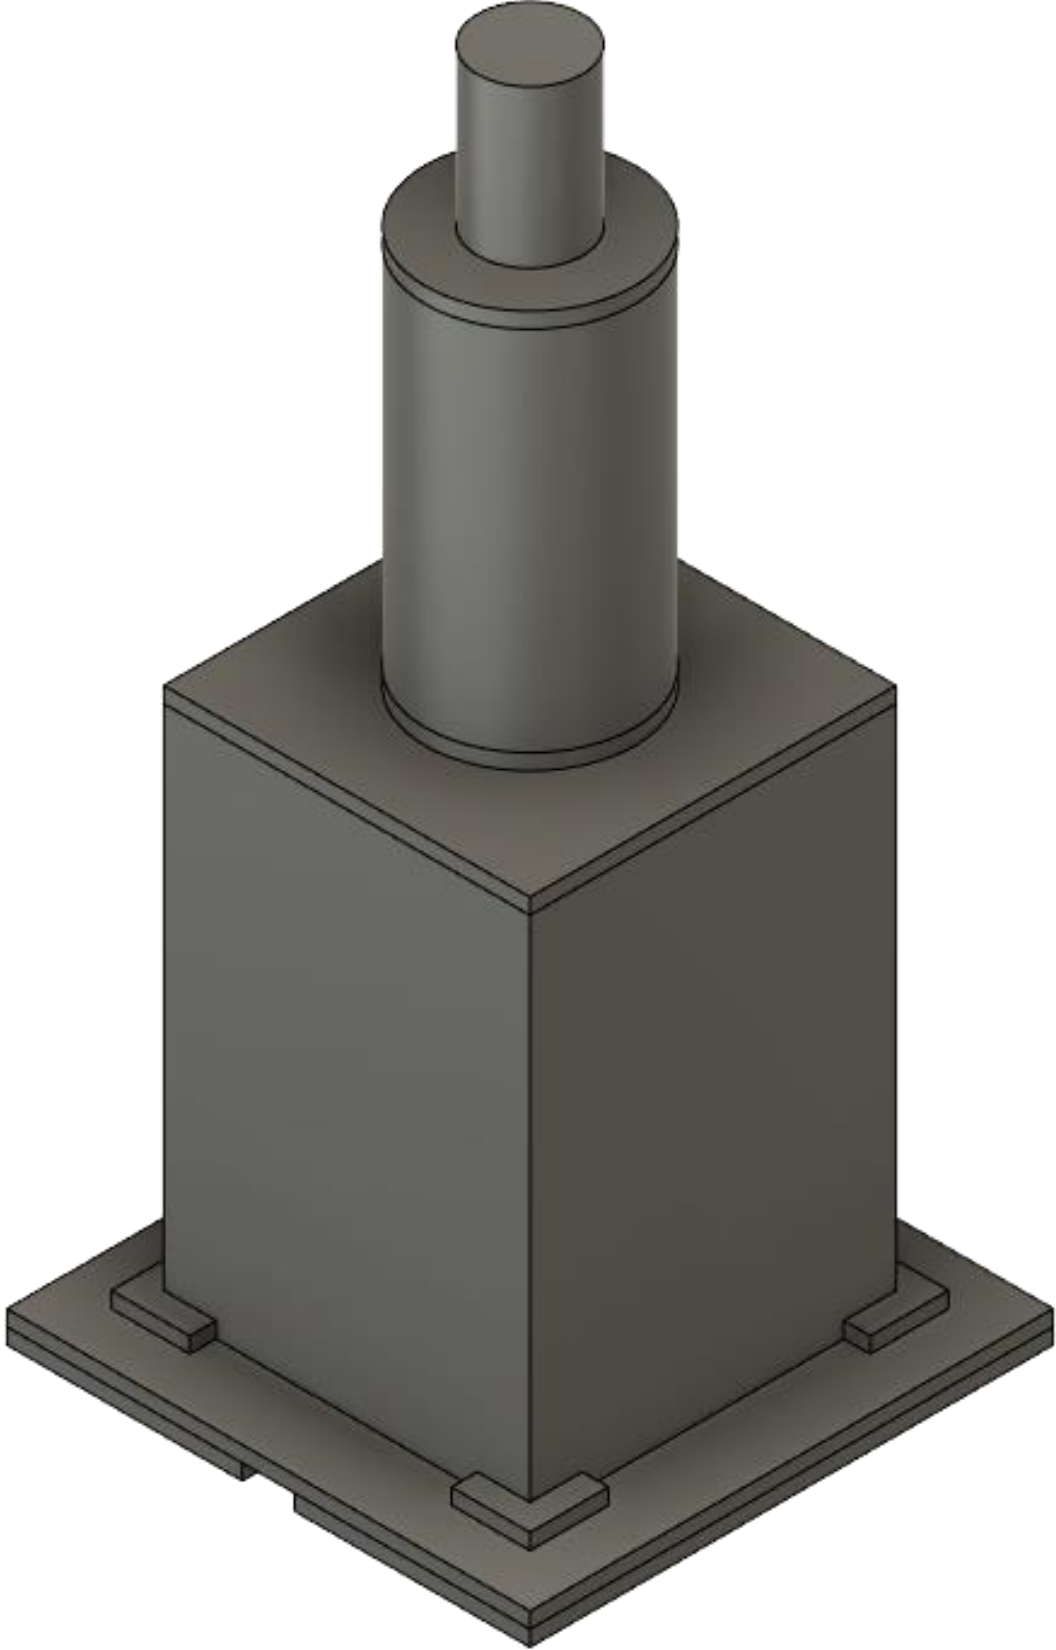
Kutu Tasarımının CAD Çizimi
